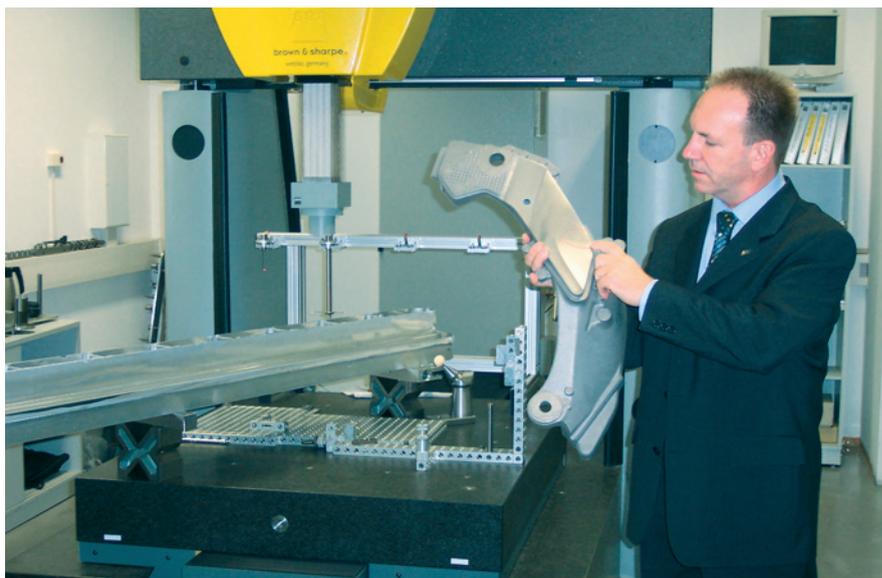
PSFU-Geschäftsführer Andreas Schubert präsentiert ein im Unternehmen bearbeitetes Gussteil
